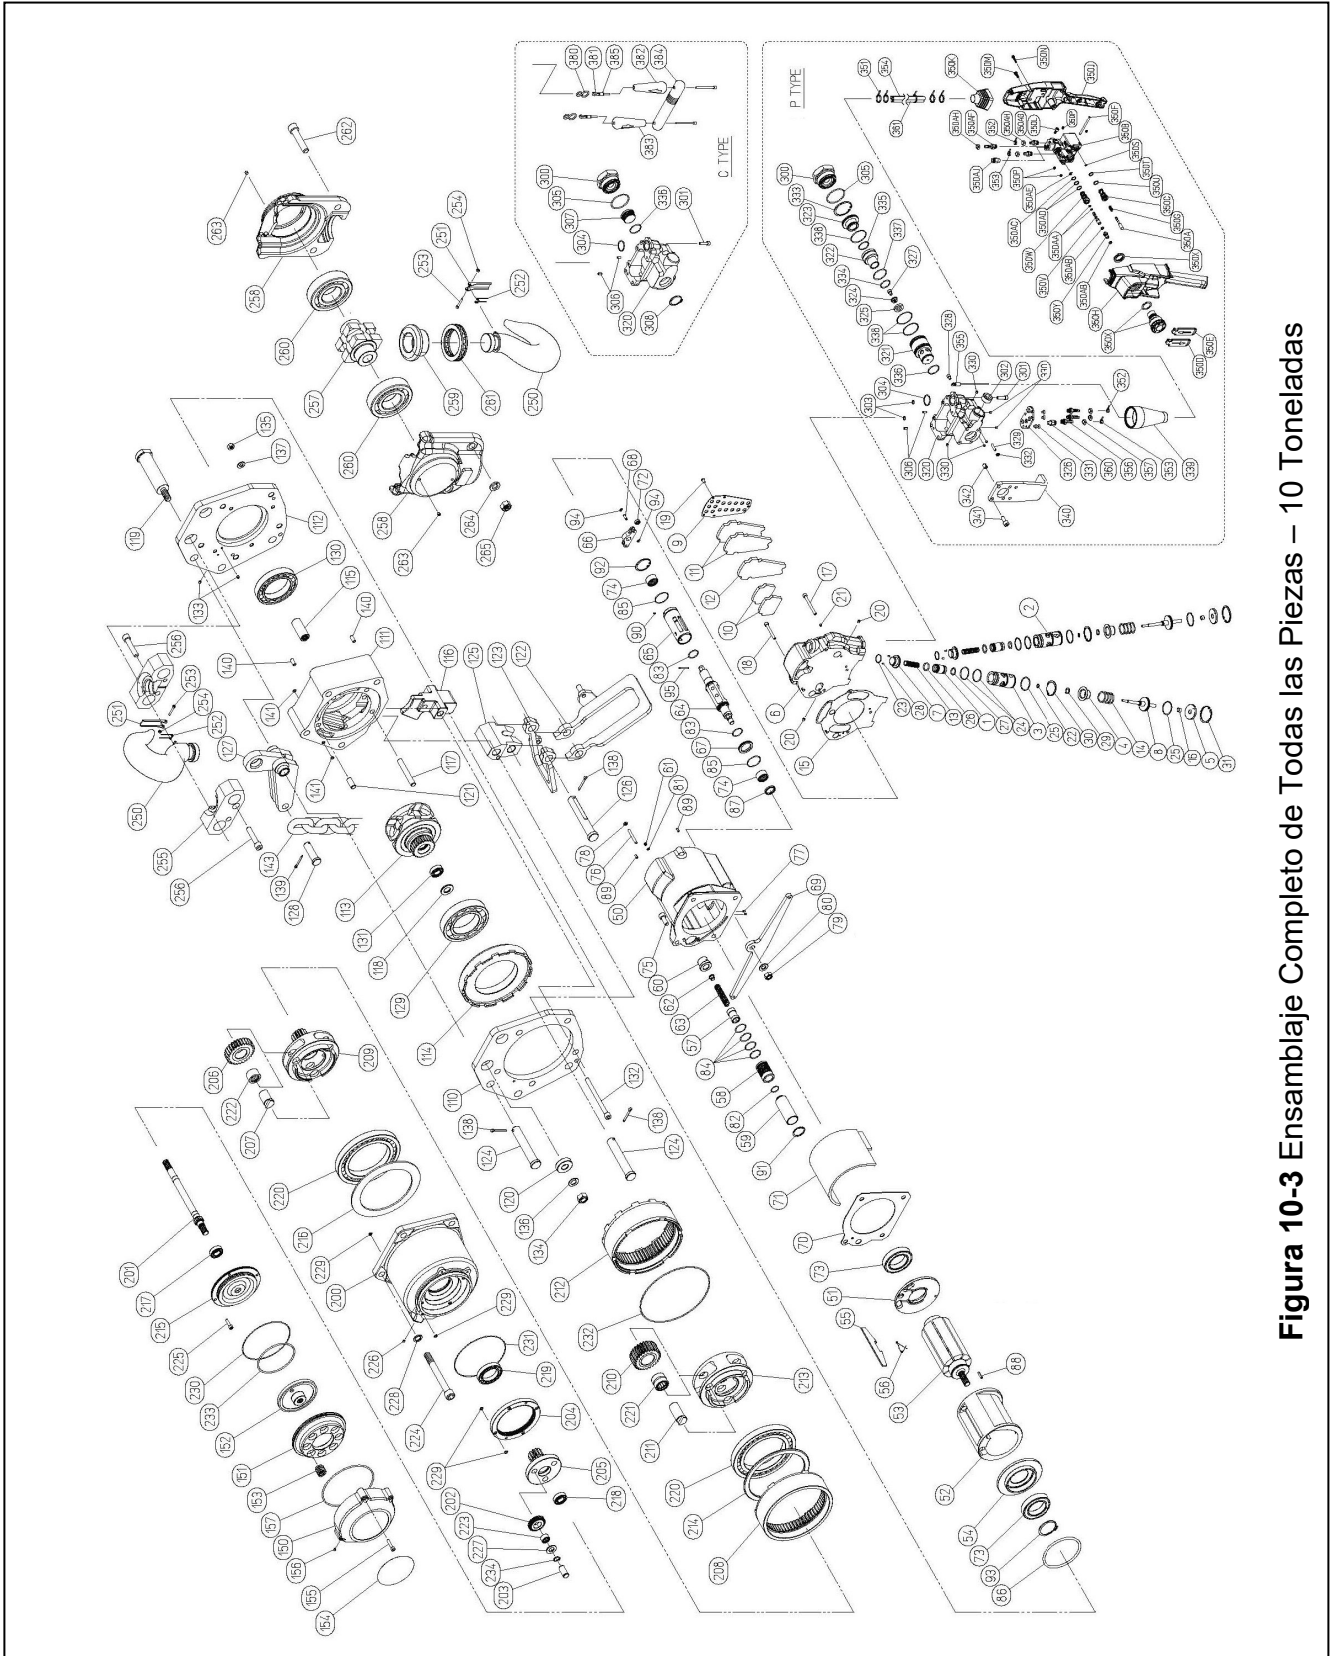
Ensamblaje Completo de Todas las Piezas – 10 Toneladas
